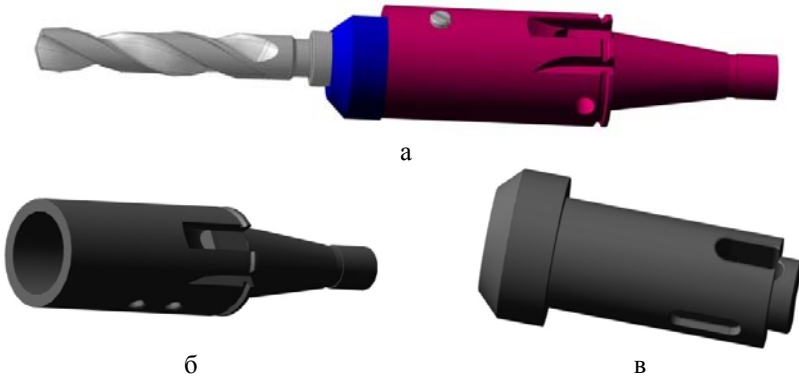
3D-моделі комплектуючих свердлильного інструментального блоку : а – інструментальний блок для свердління; б – утримувач; в – втулка перехідна
